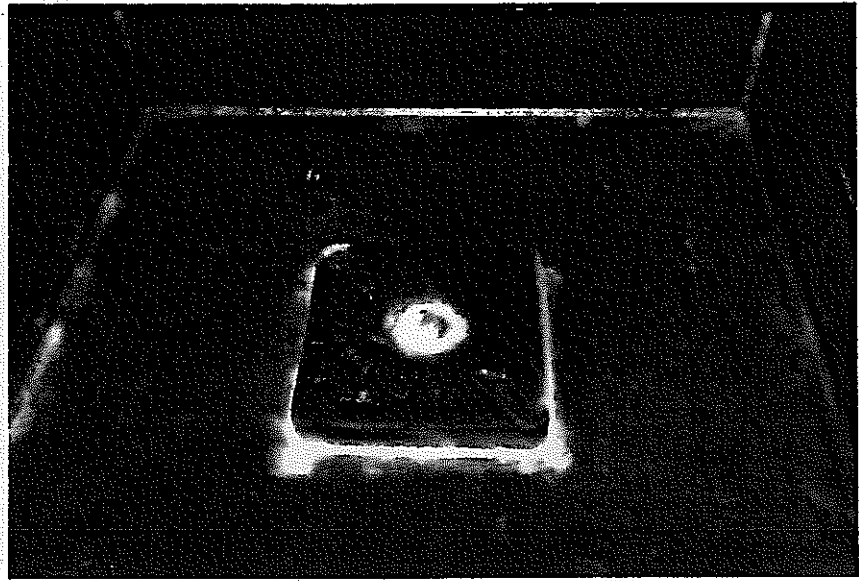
溶接部の液体浸透探傷検査
